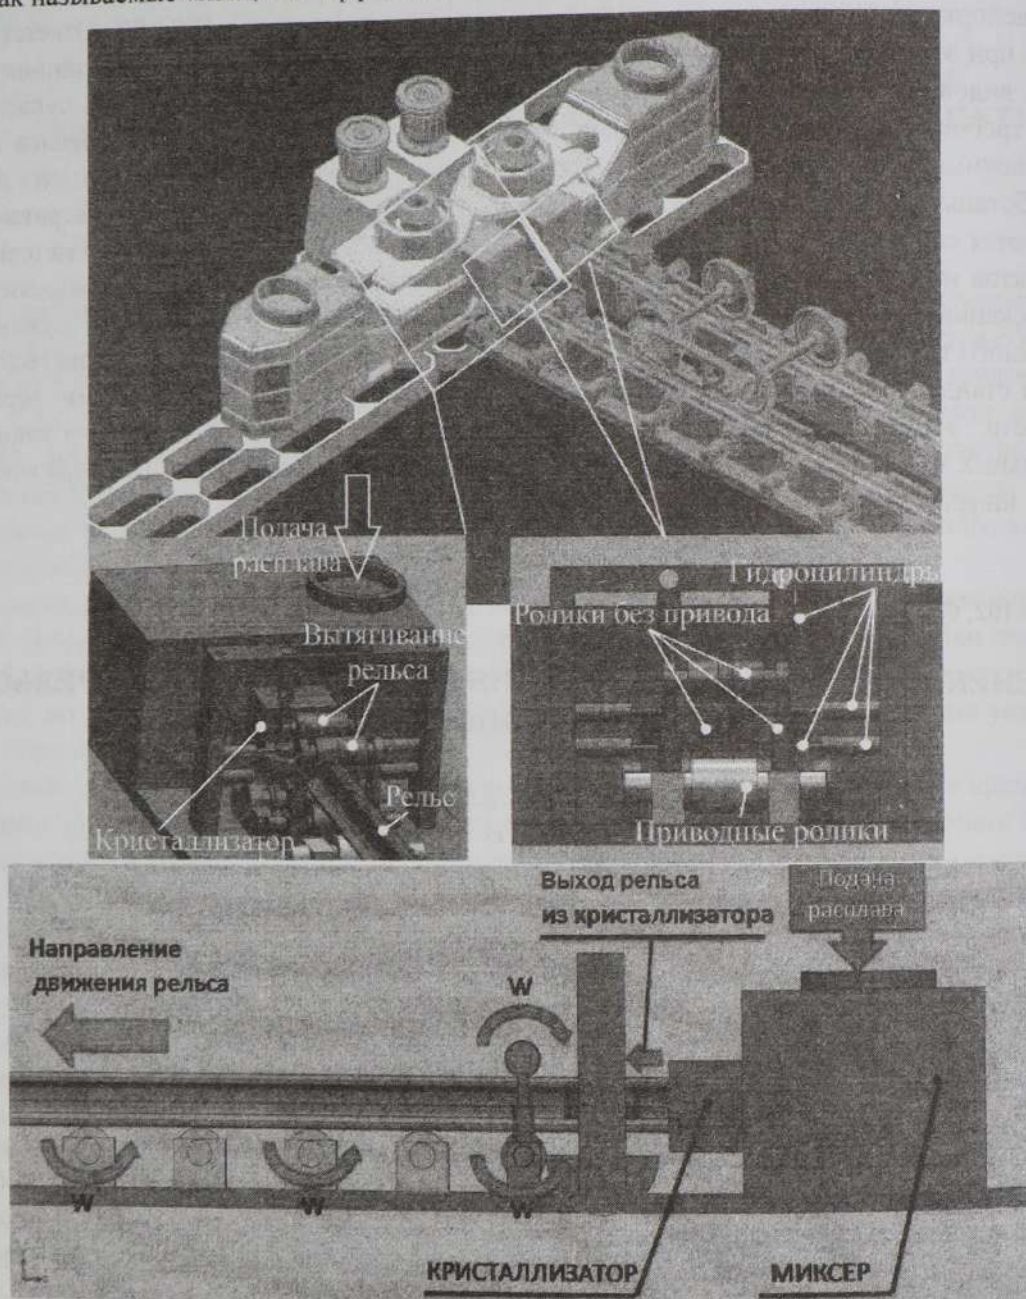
Схема установки для непрерывной отливки чугунных рельсов
